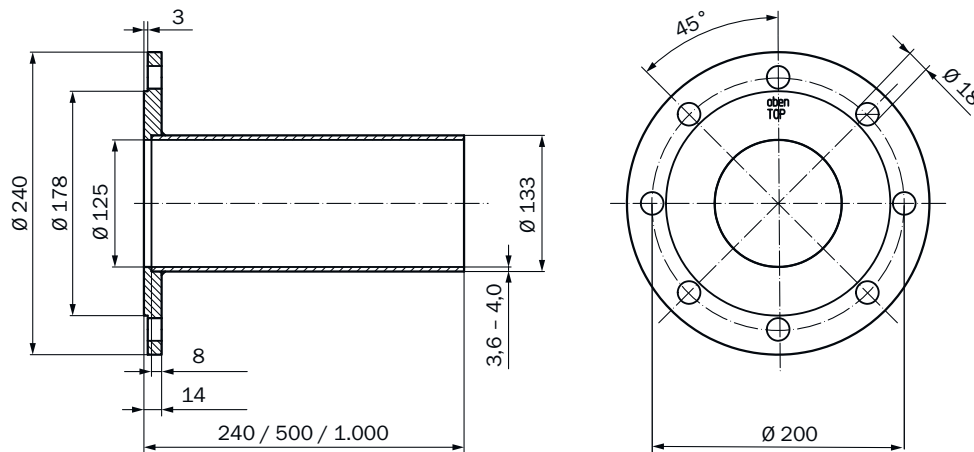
Flansch mit Rohr DN125 (Maße in mm)
